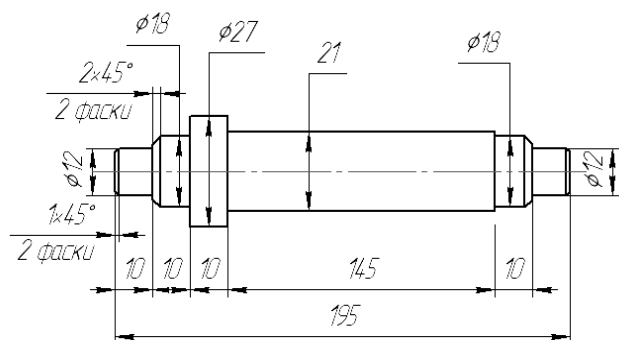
Оправка для выпрессовки и запрессовки гнезда перепускного клапана.
